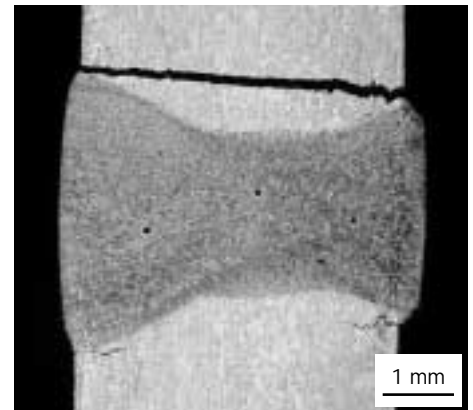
Querschliff - Anrisse an einer unbearbeiteten Schweißnaht, ausgehend von Einbrandkerben
